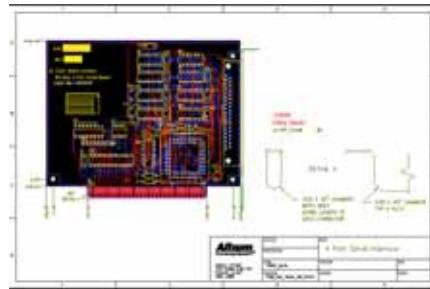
Kształt płyty musi być zdefiniowany dla każdego projektu PCB - możemy go zmienić używając poleceń z menu *Design>Board Shape
